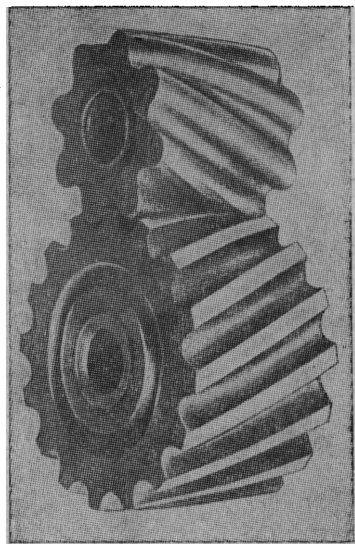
Цилиндрические зубчатые колеса с заплосным зацеплением.
